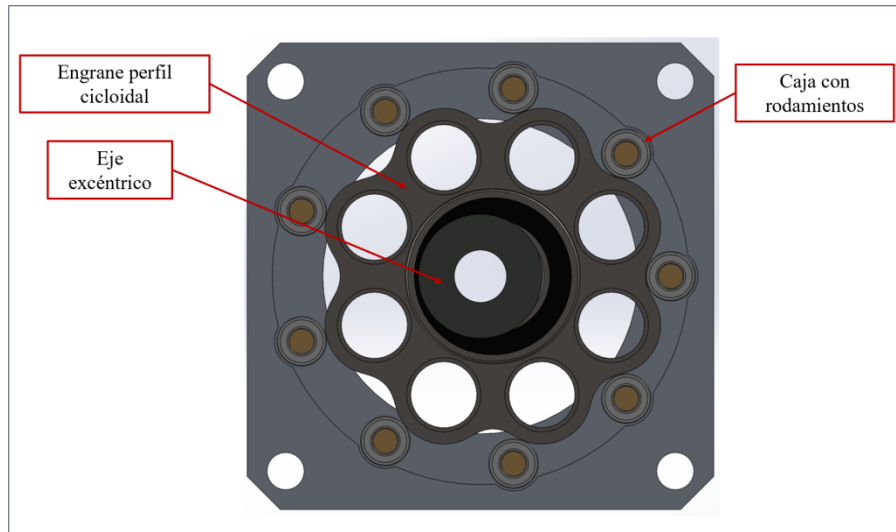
Corte de sección del ensamblaje del reductor cicloidal.
